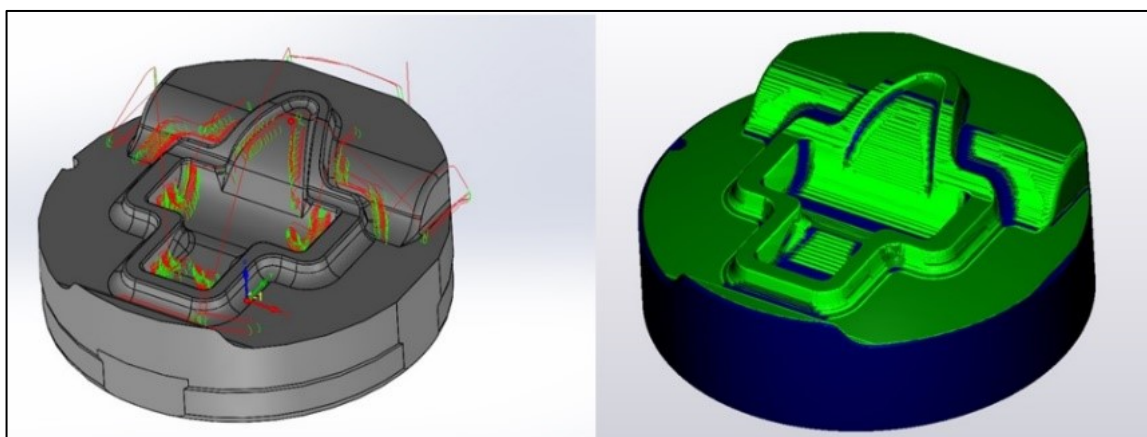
Dráhy hrubování D20, kontrola přidavků po hrubování
